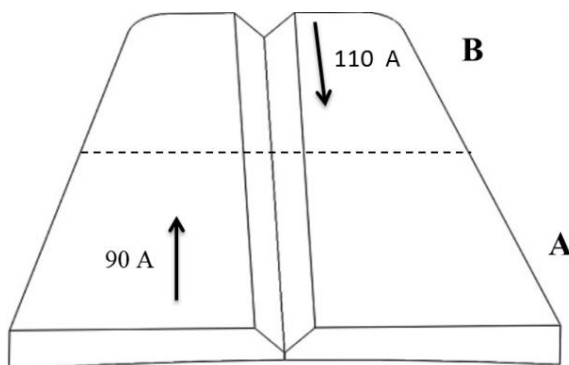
Esquema do procedimento de soldadura.
